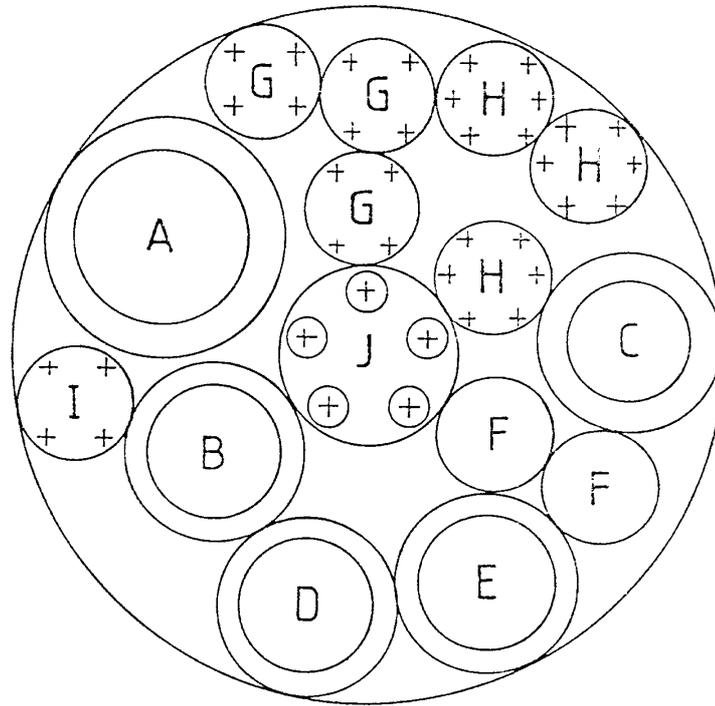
Corte transversal del umbilical de la Torreta.
